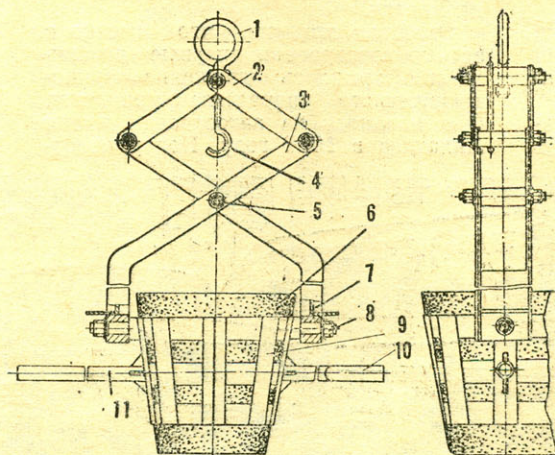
Схема захвата: 1 — серьга, 2, 3 — рычаги зажима, 4 — крюк, 5 — палец, 6 — тигель, 7 — козырек оси, 8 — ось полукорзины, 9 — полукорзина, 10, 11 — ручки-рычаги.
